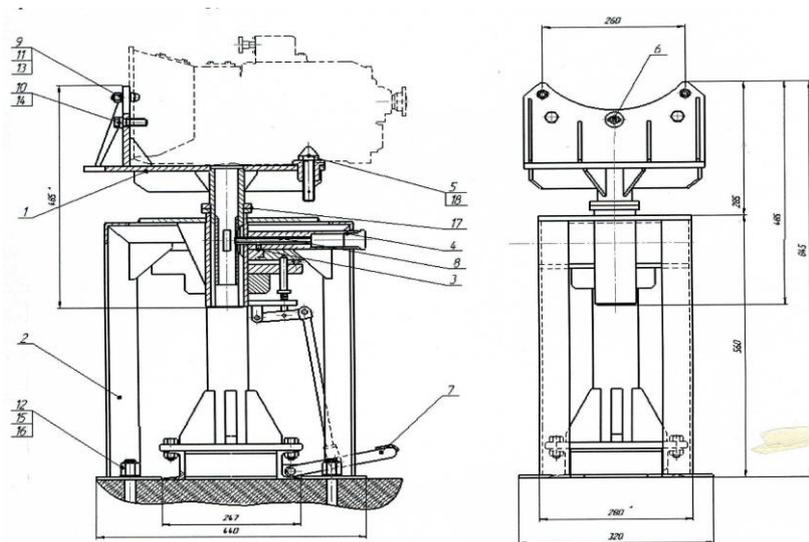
Стенд для операций разборки-сборки КПП автомобилей
